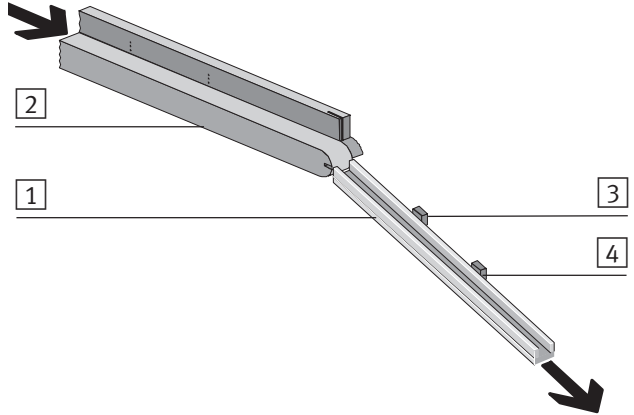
/2: Staustrecken-Kontrolle mit Schaltverzögerung
